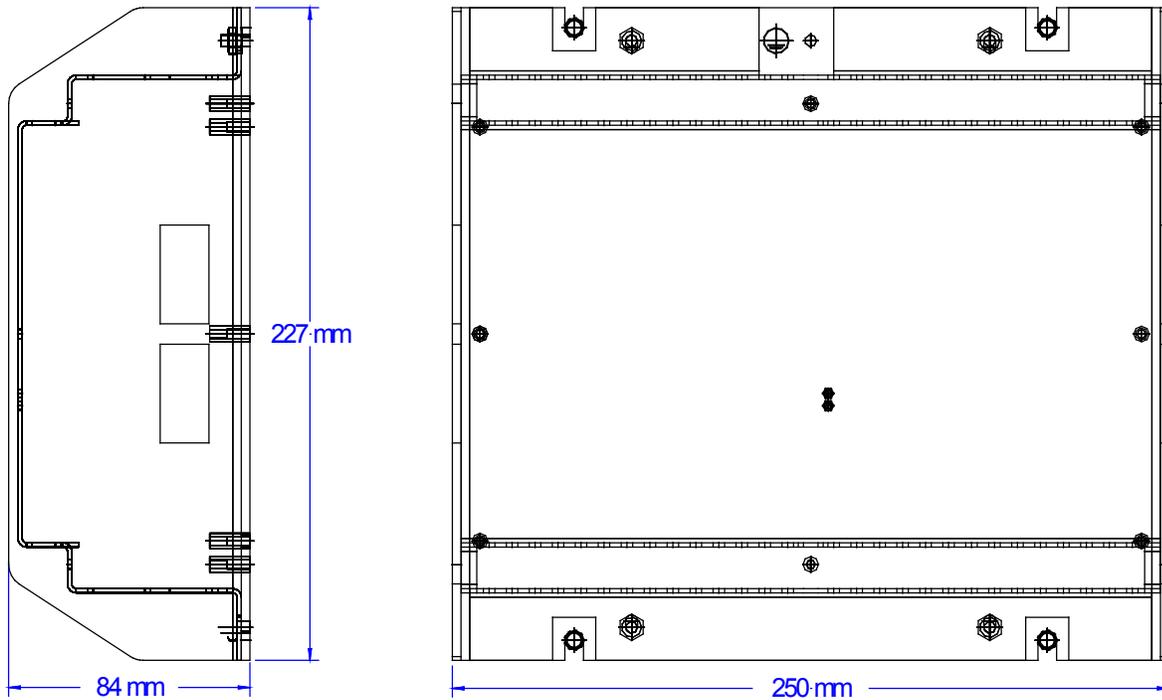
Metallgehäuse easYgen-3000 - Abmessungen
